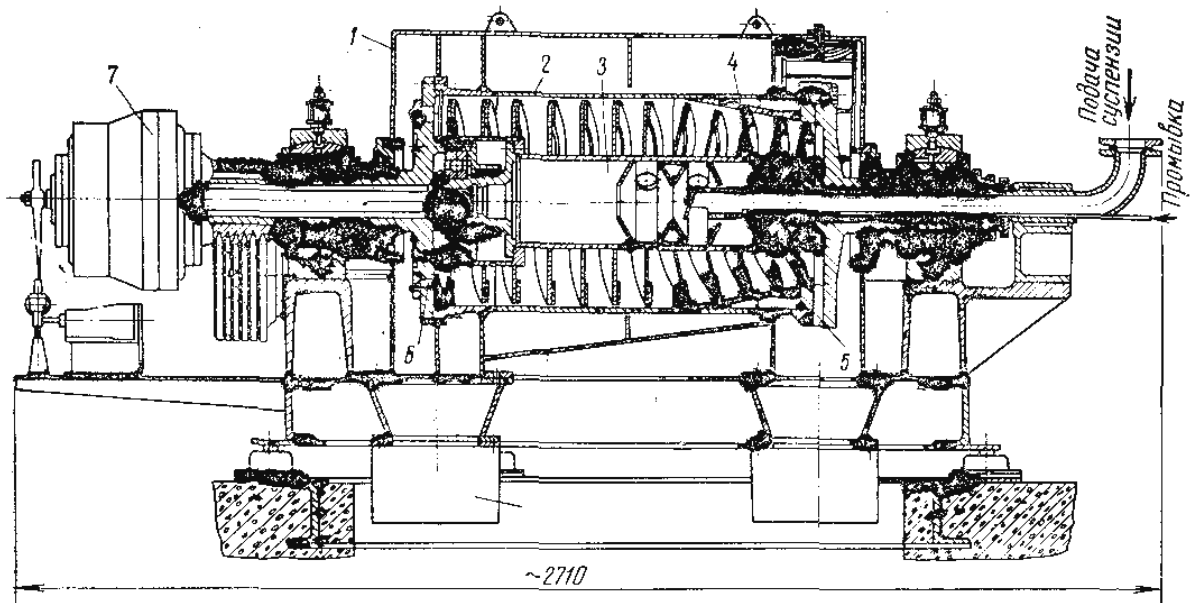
Центрифуга марки ОГШ-352. 1- кожух, 2- зовнішній барабан 3- внутрішній барабан, 4- шнек, 5 сопла для тяжкої фракції, 6 – отвір для легкої фракції, 7- планетарний редуктор.
